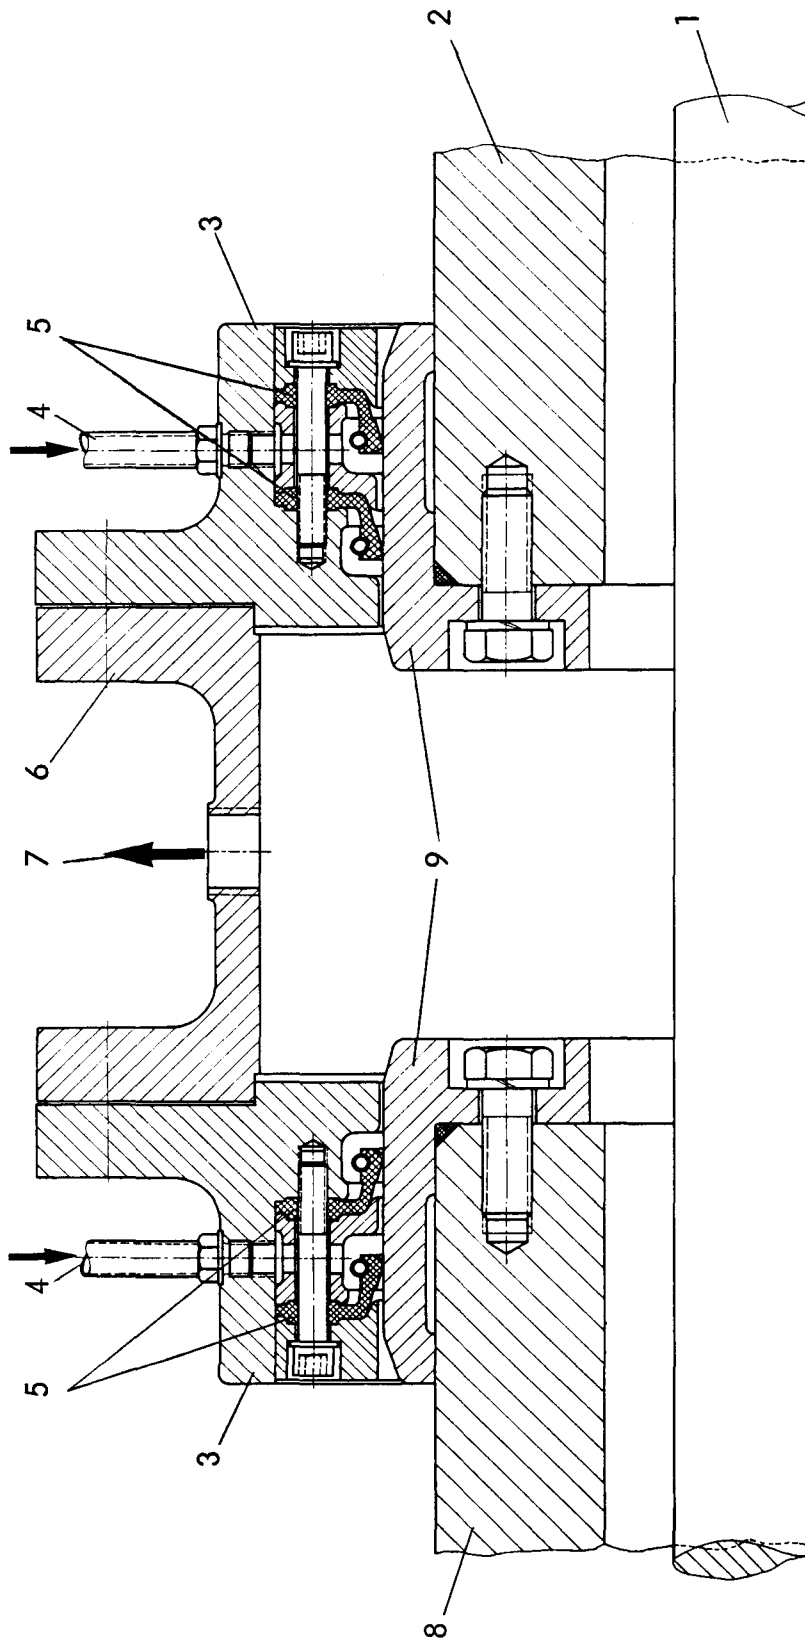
Innenwellen-Innendichtung für den Einbau zwischen den Getrieben
